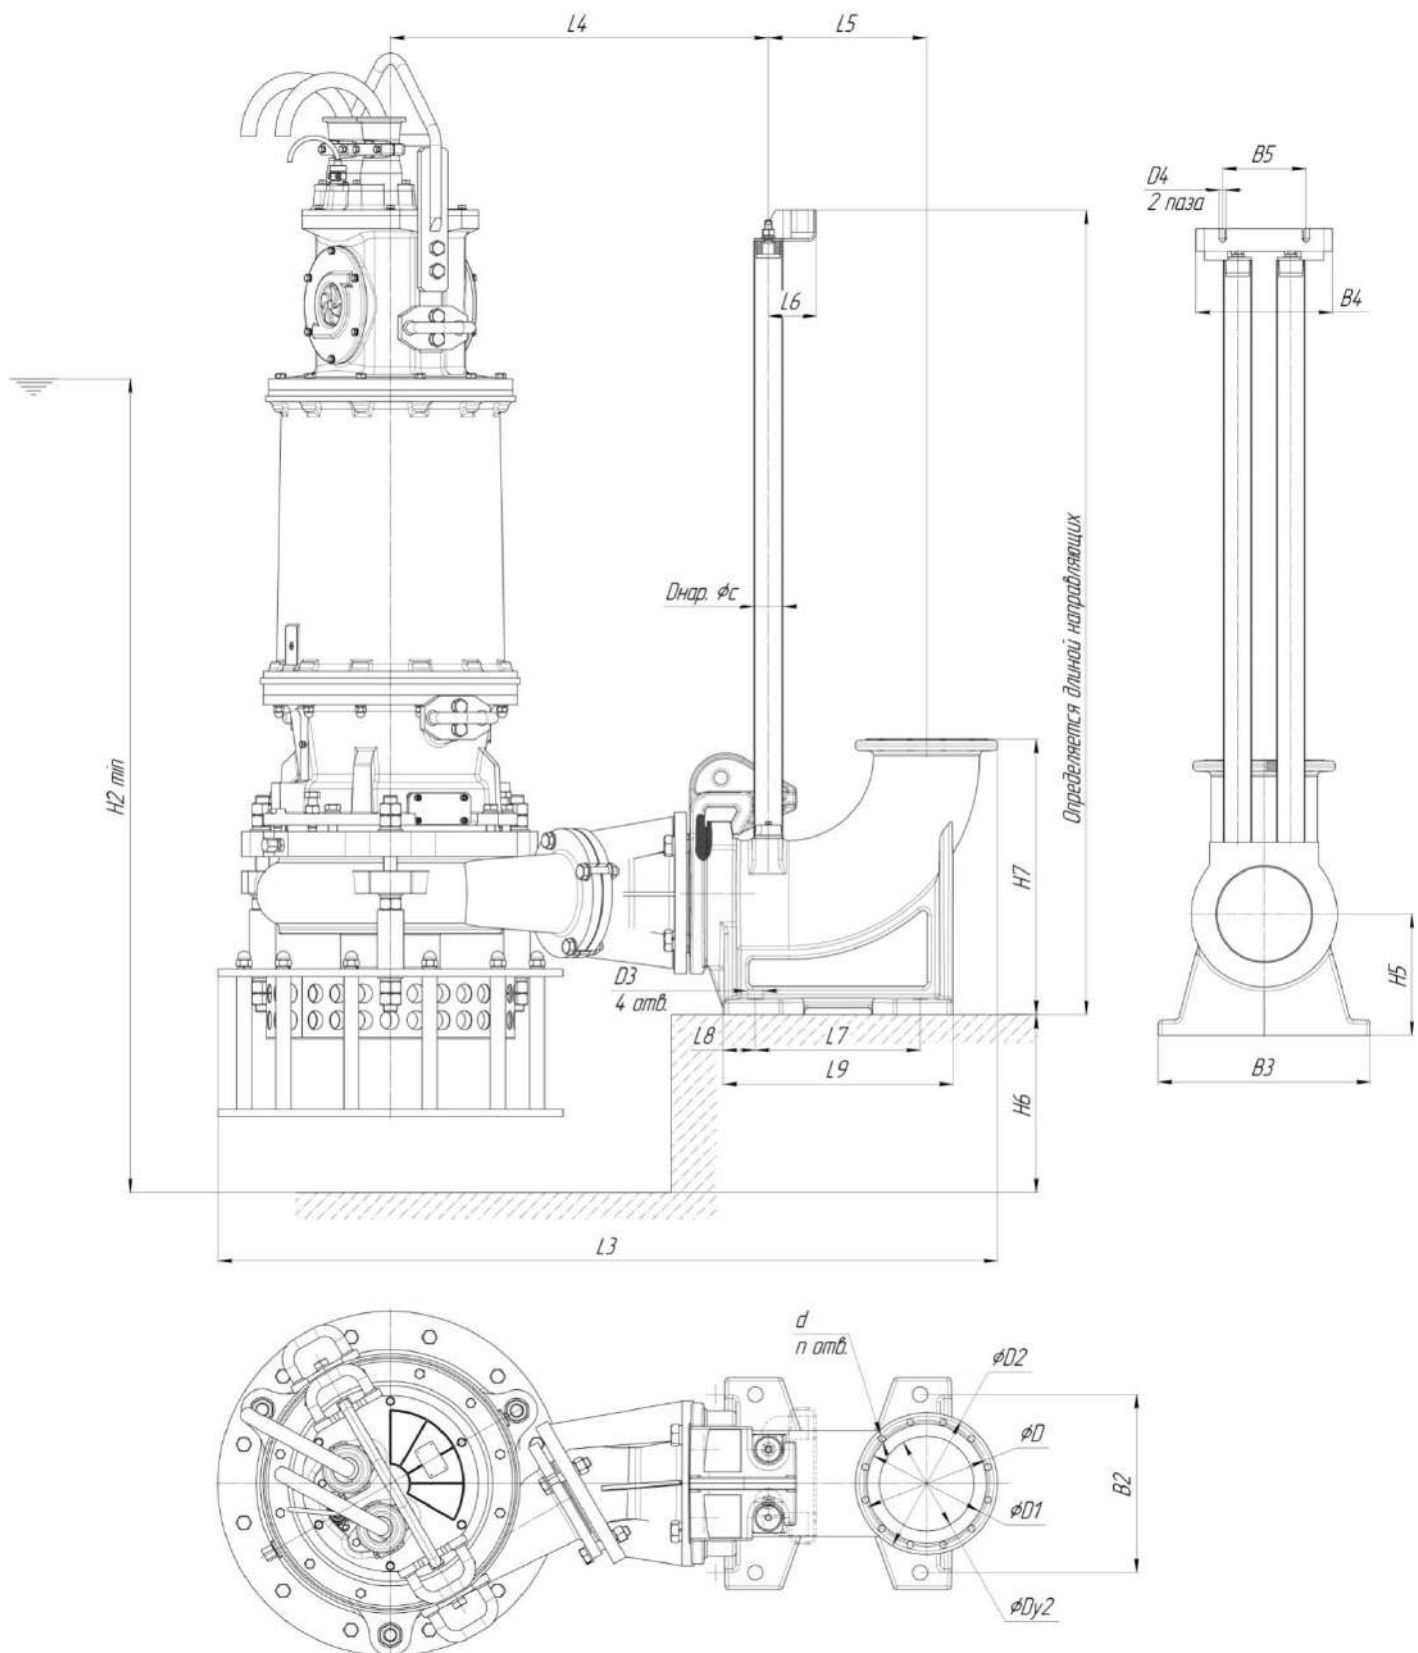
Схема общего вида, габаритные и присоединительные размеры электронасоса «Иртыш» ПШ 160-250 кВт – 106
